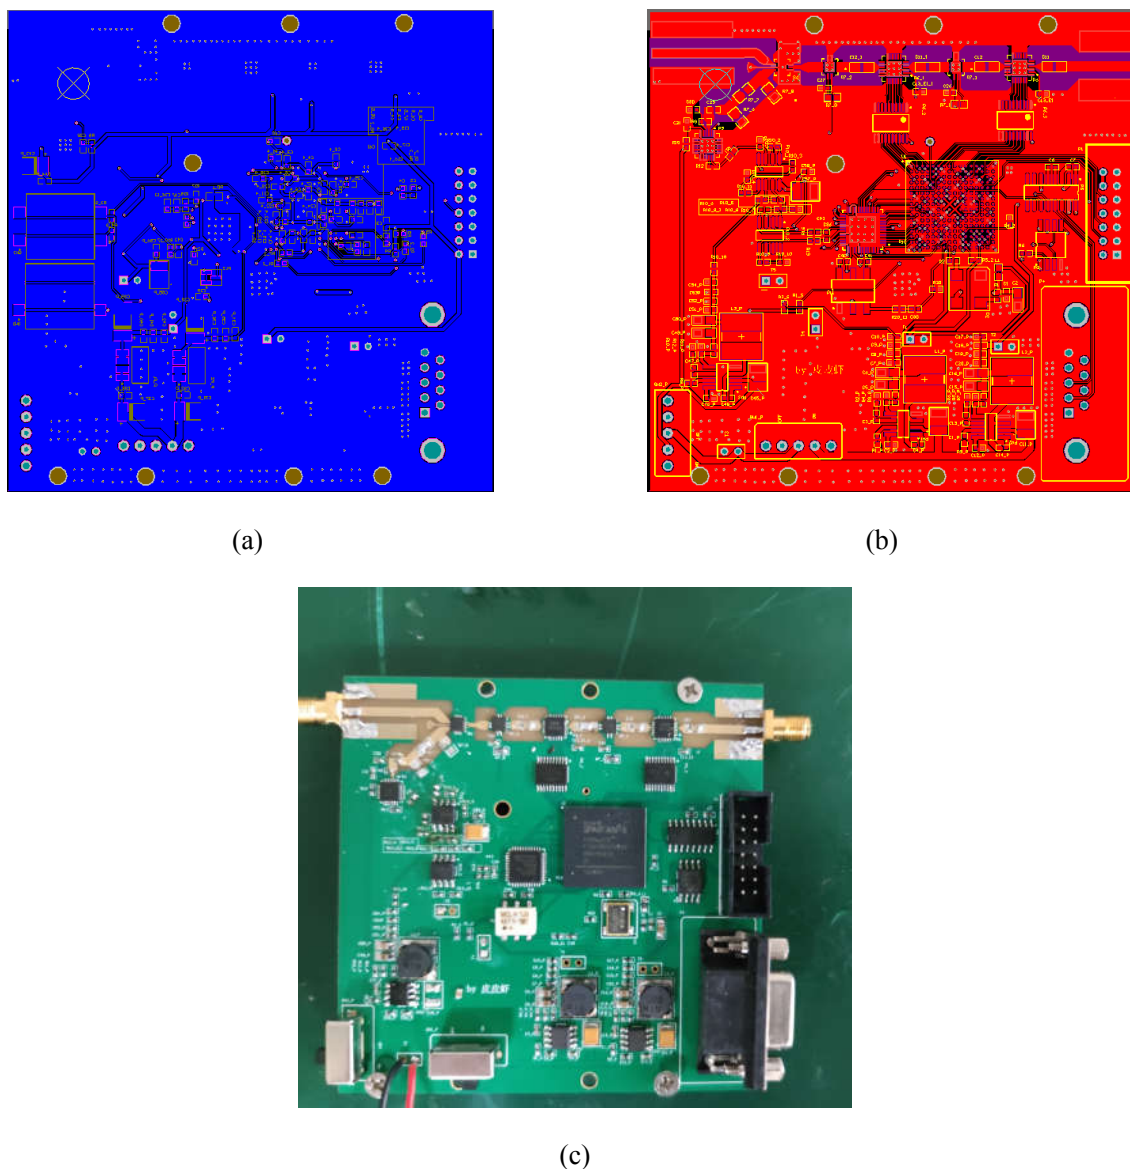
数字 AGC 系统 PCB 版图。(a) PCB 板 bottom 层；(b) PCB 板 top 层；(c) PCB 板实物
